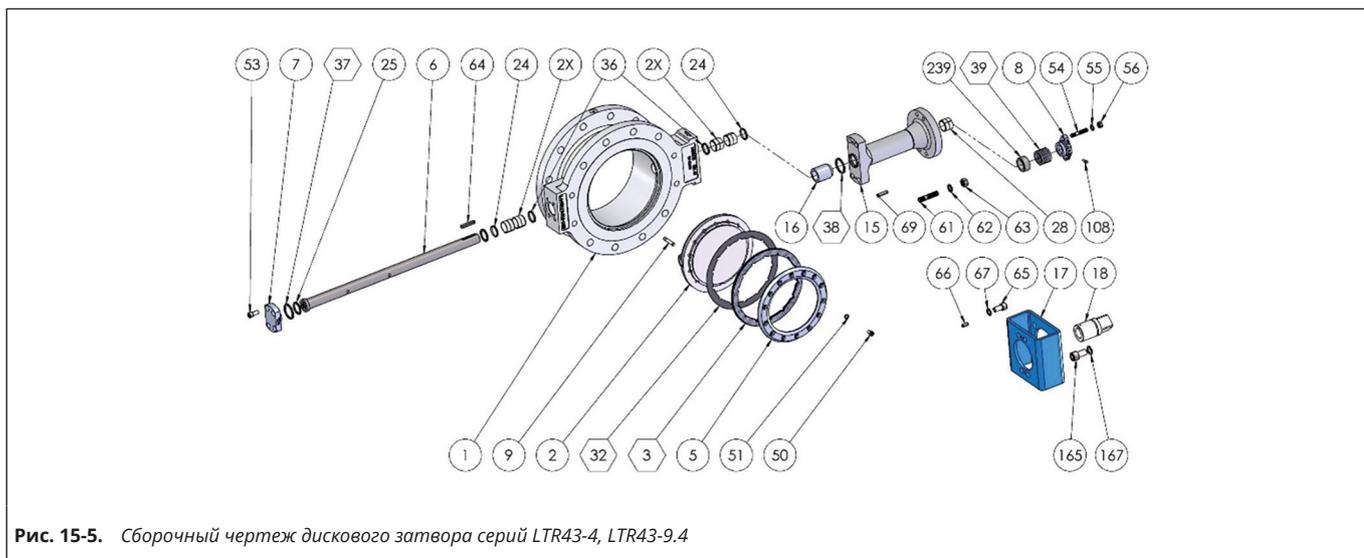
Сборочный чертеж дискового затвора серий LTR43-4, LTR43-9.4
